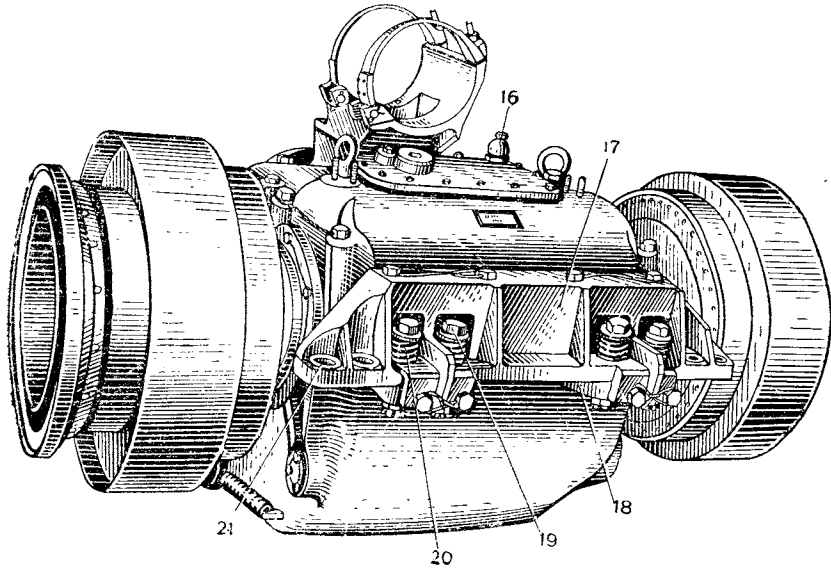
Коробка передач с механизмами поворота (общий вид сзади):
